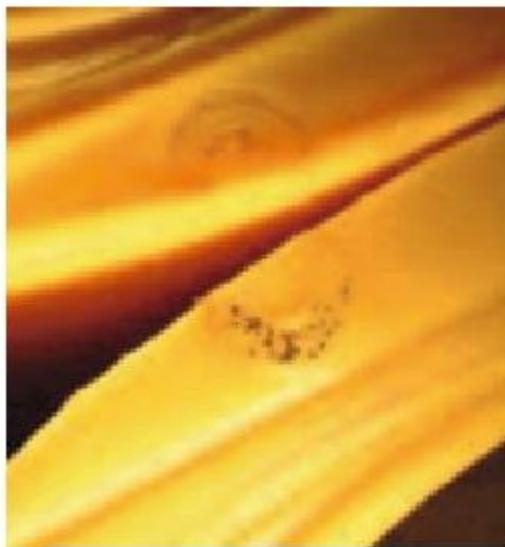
Растрескивание под напряжением в результате загрязнения сварного шва
